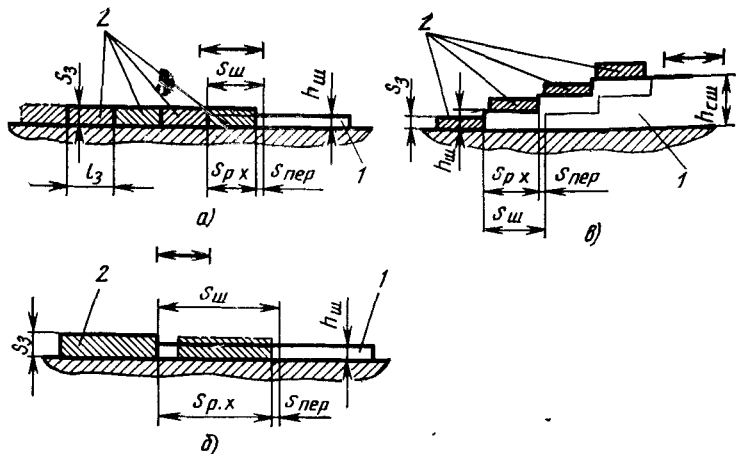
Способы подачи заготовок шиберными подающими устройствами
